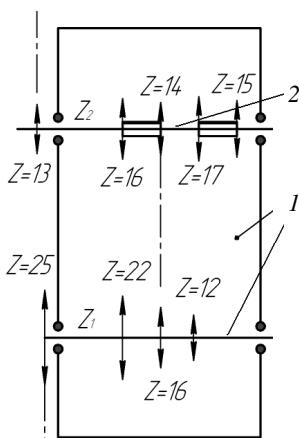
Схема цепного редуктора высаживающего аппарата:
